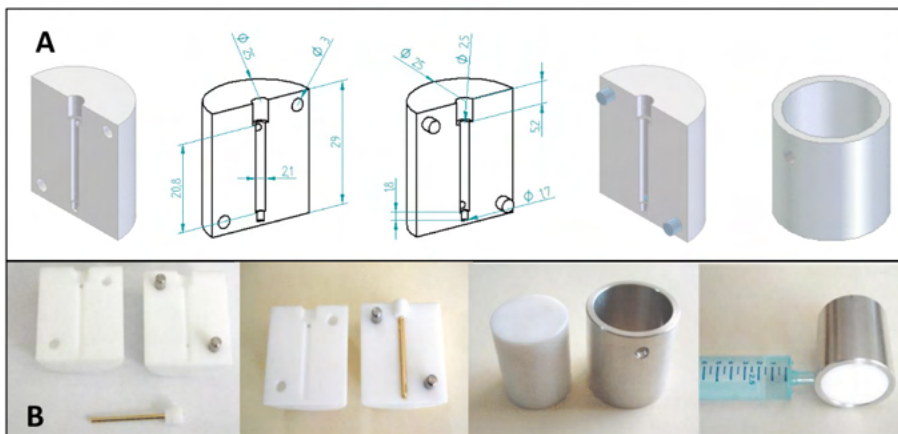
Projeto do molde para barras e “holder”. (A) Desenho técnico em três dimensões (3D) do molde e Holder; (B) Execução Mecânica e Montagem do Conjunto.
